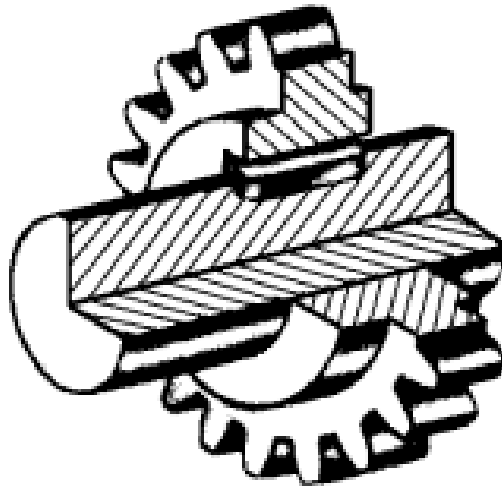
Шпонкове з'єднання шестерні з валом
